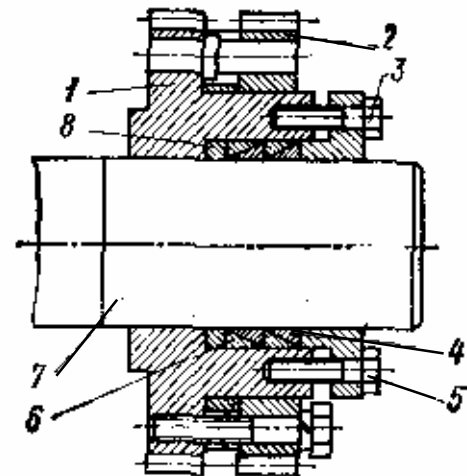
Схема безшпонкового з'єднання зубчатого колеса з валом
